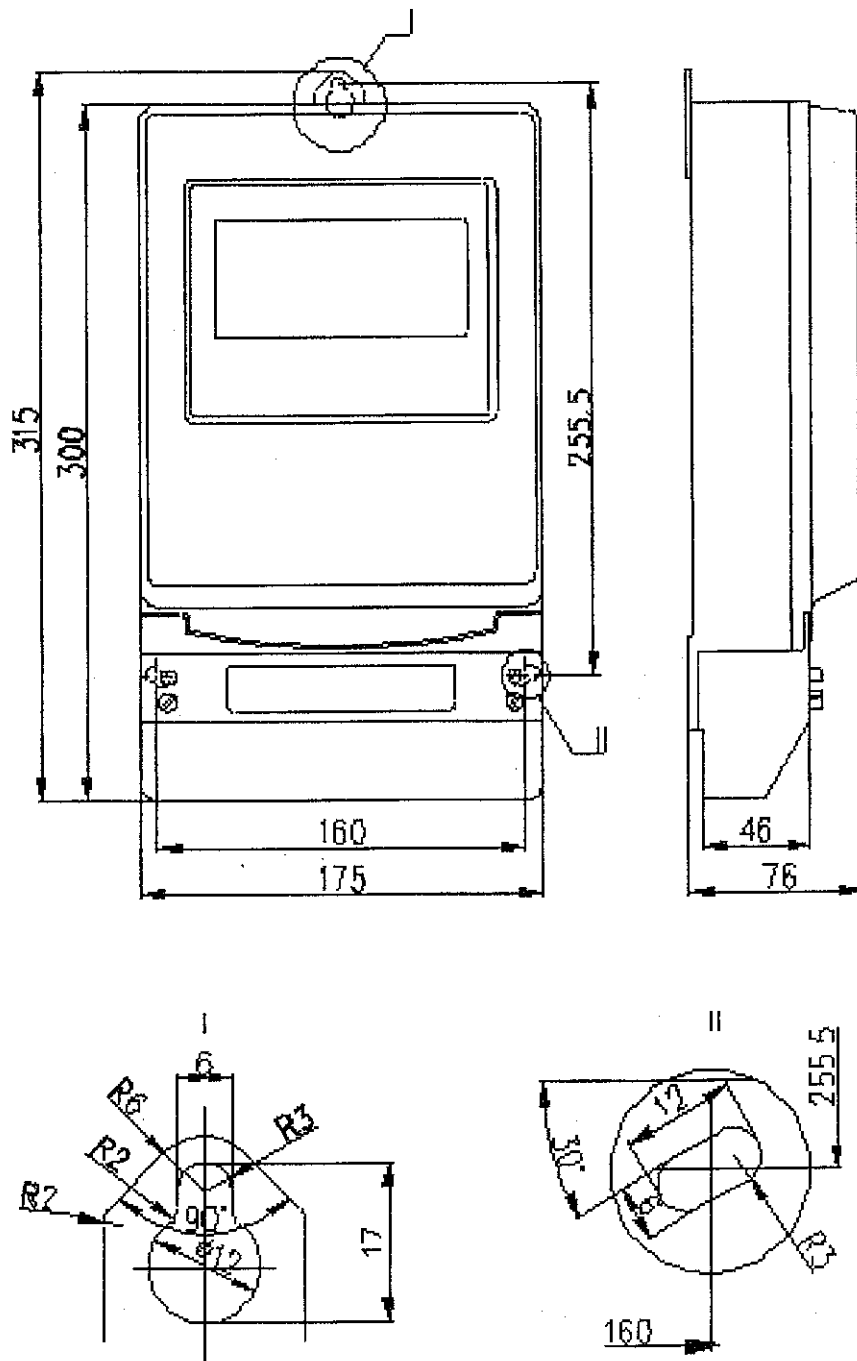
Габаритные и установочные размеры устройства «УСПД-Нейрон»
